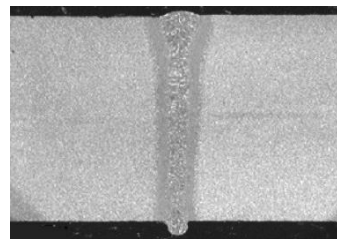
Образец сварки с глубоким проплавлением
